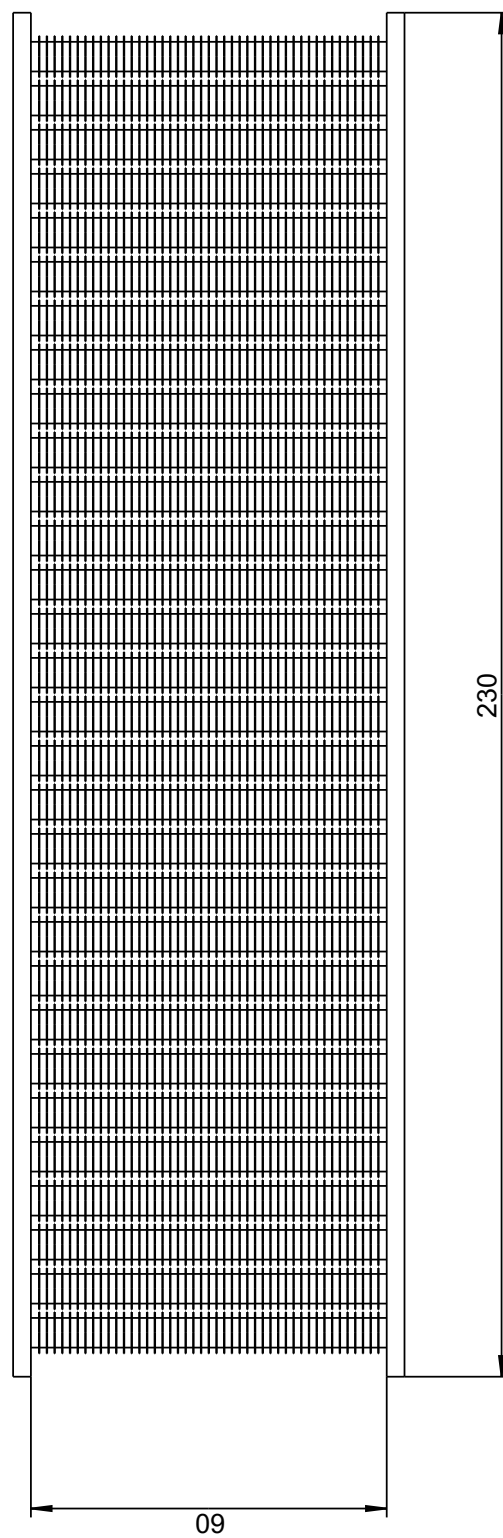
Abgasseitige Anströmung des Rippenrohrbündeldampferzeugers *RRB-Eth-14230
